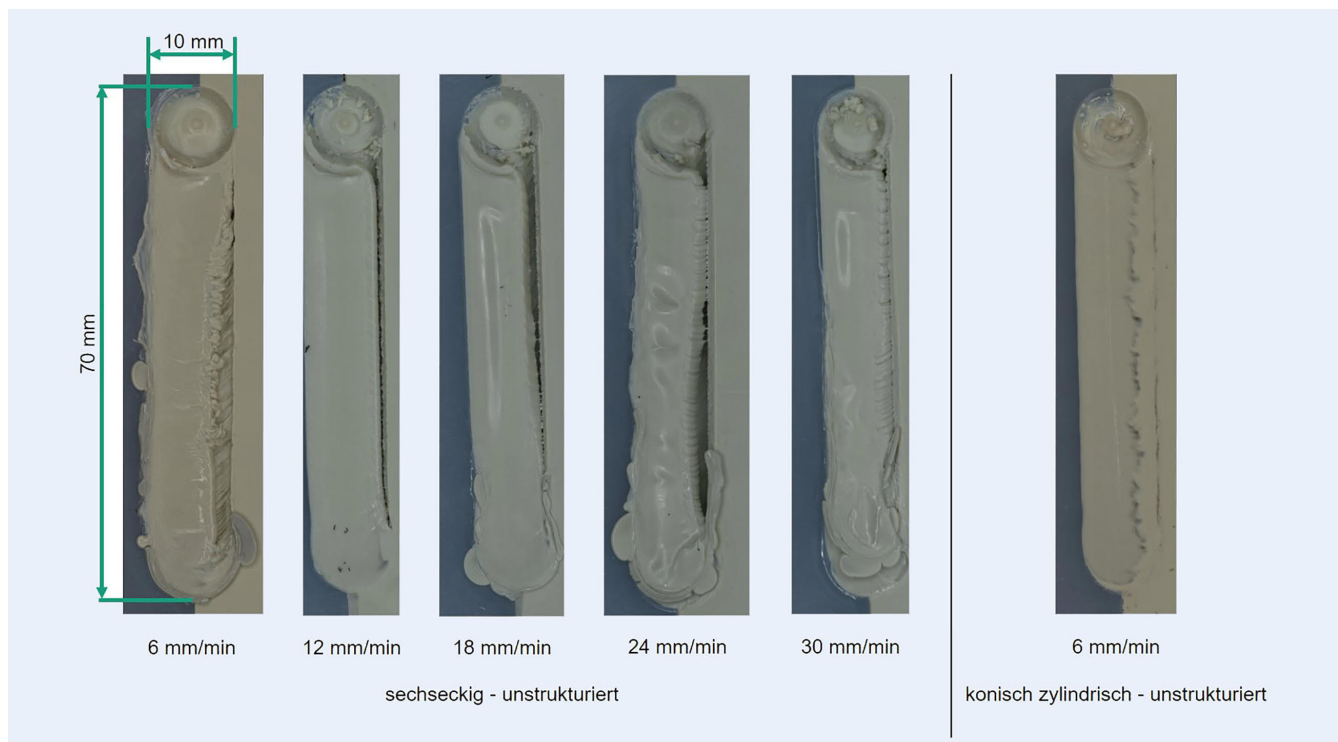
Schweißnähte des sechseckigen Werkzeuges über steigende Vorschübe (links) und des konischen zylindrischen Werkzeuges mit 6 mm Vorschub (rechts). Foto: Fraunhofer IPA
